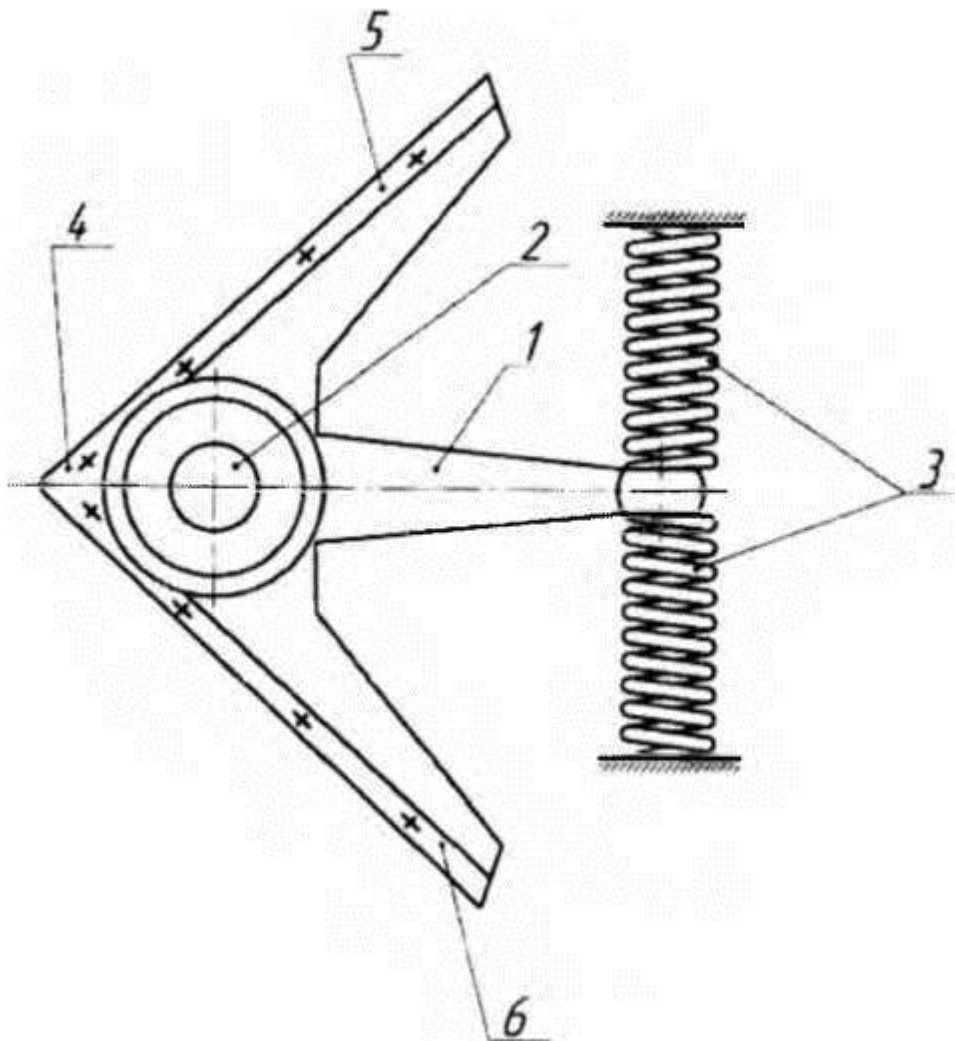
Робочий орган культиватора [7], вид зверху
